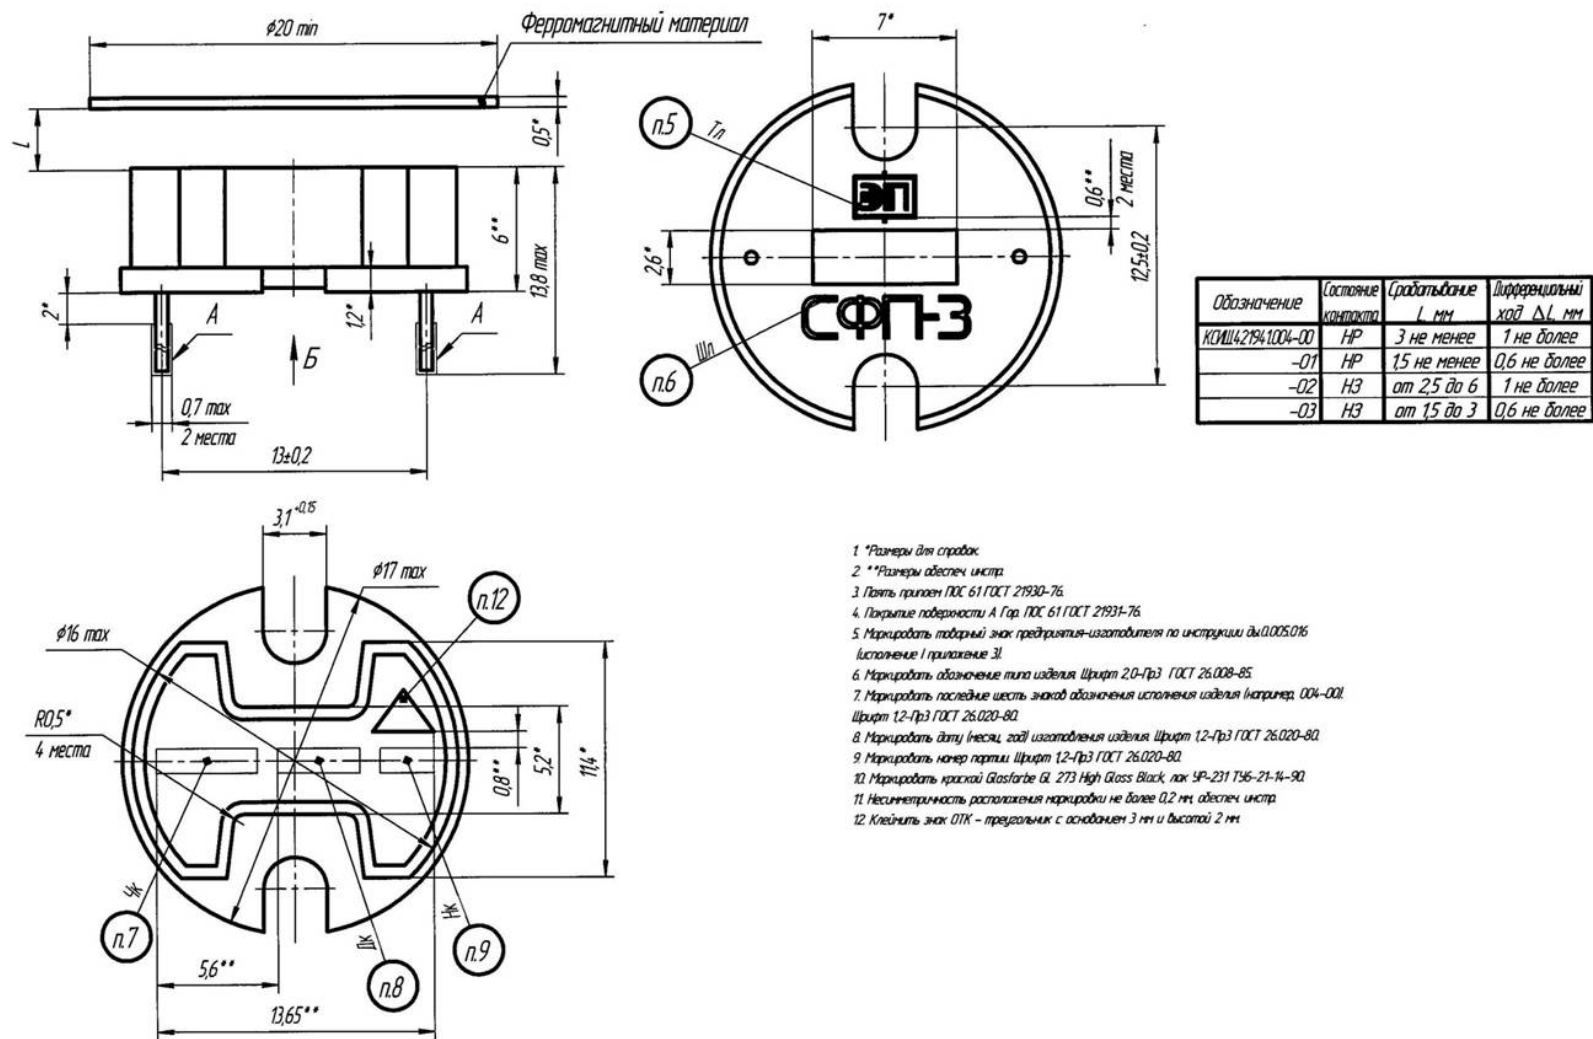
Габаритный чертеж сигнализатора СФП-3
